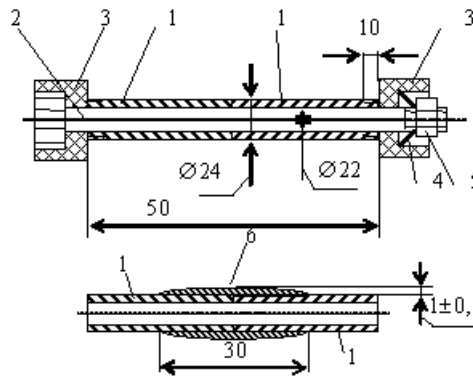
Схема пристрою для нанесення покриття на зразок для визначення когезії ЕДП за розтягу: 1 – дві частини зразка; 2 – штифт; 3 – захисні шайби; 4 – пружина; 5 – гайка; 6 – покриття.
